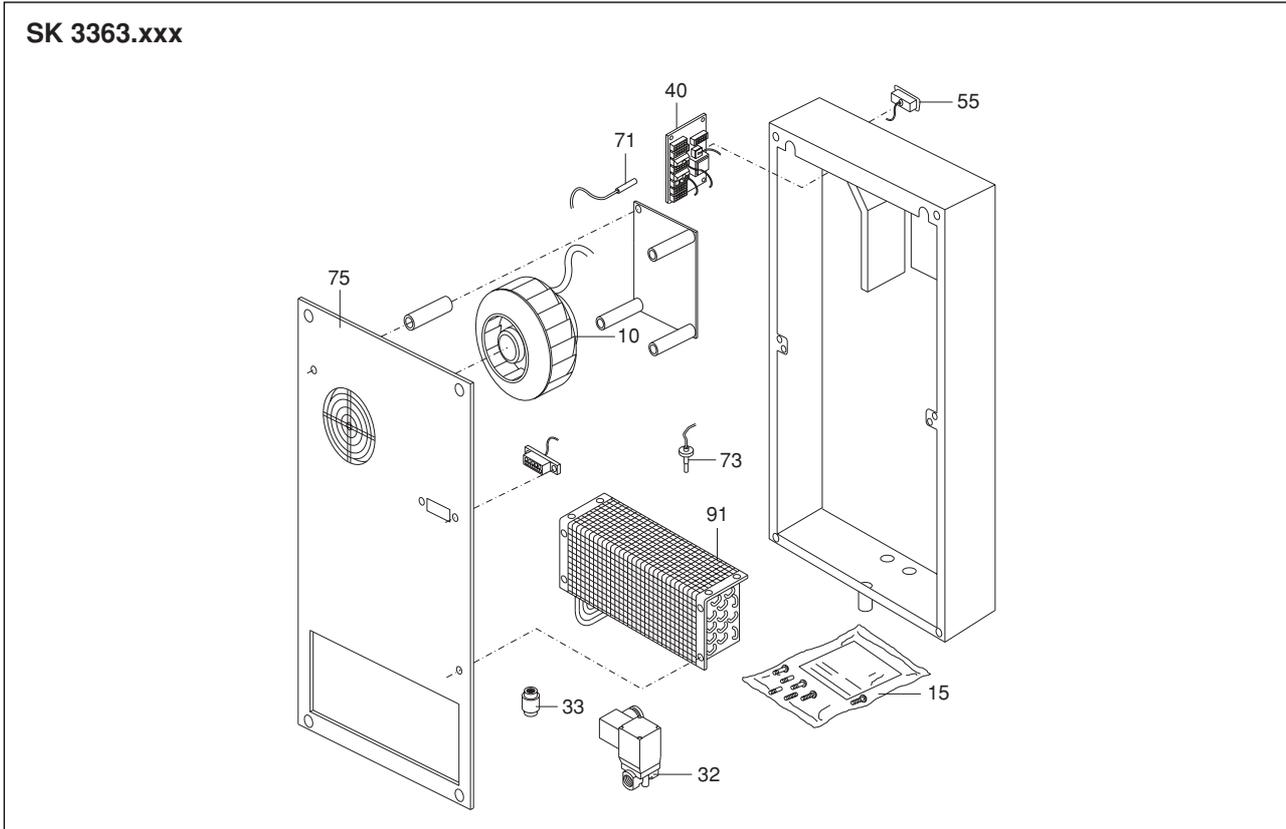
Pièces de rechange pour SK 3363.xxx
